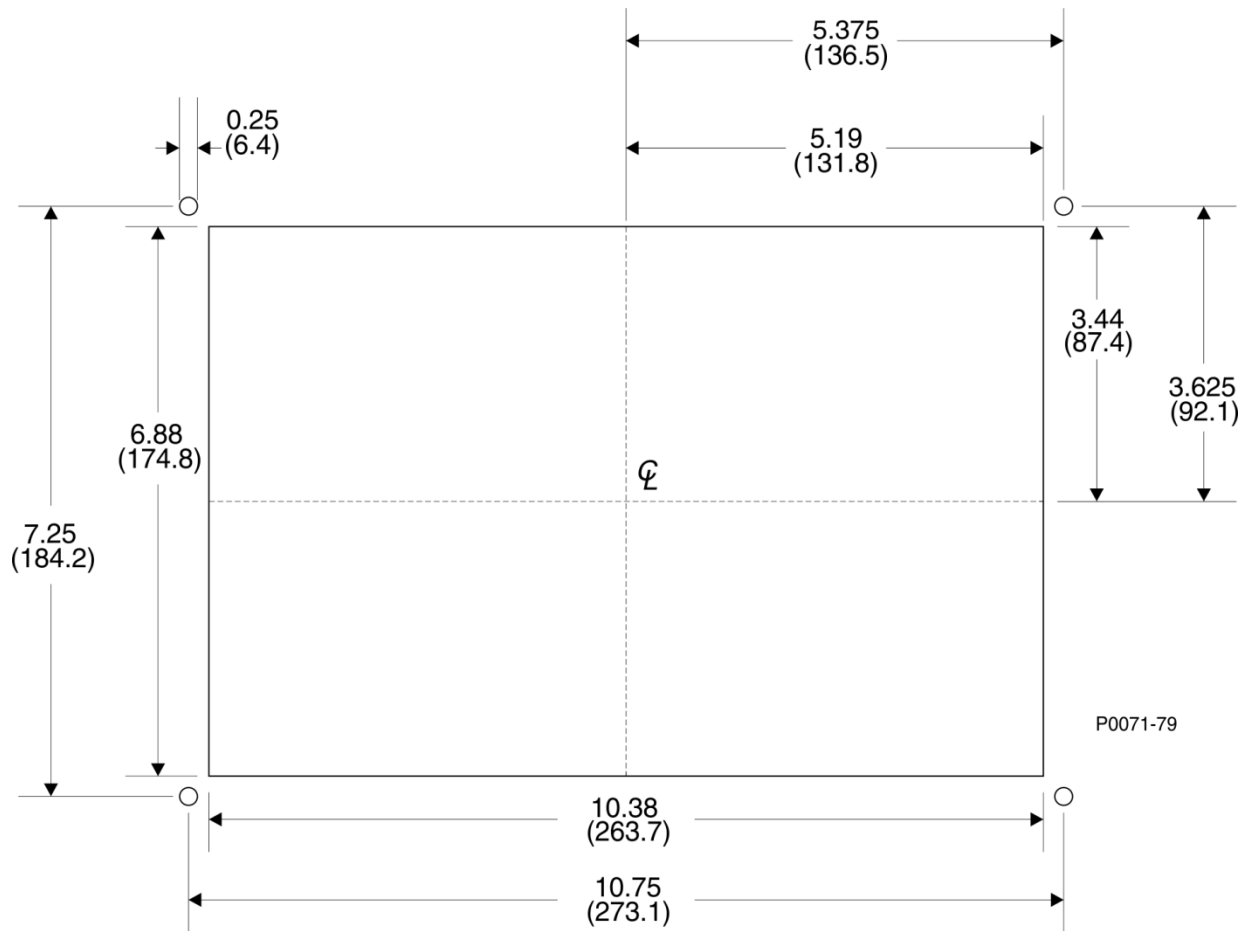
Ausschnitt- und Bohrmaße für Frontplattenmontage
